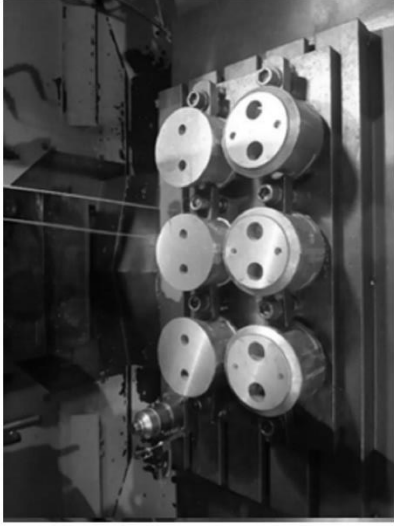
Базування та закріплення заготовок для фрезерної обробки
